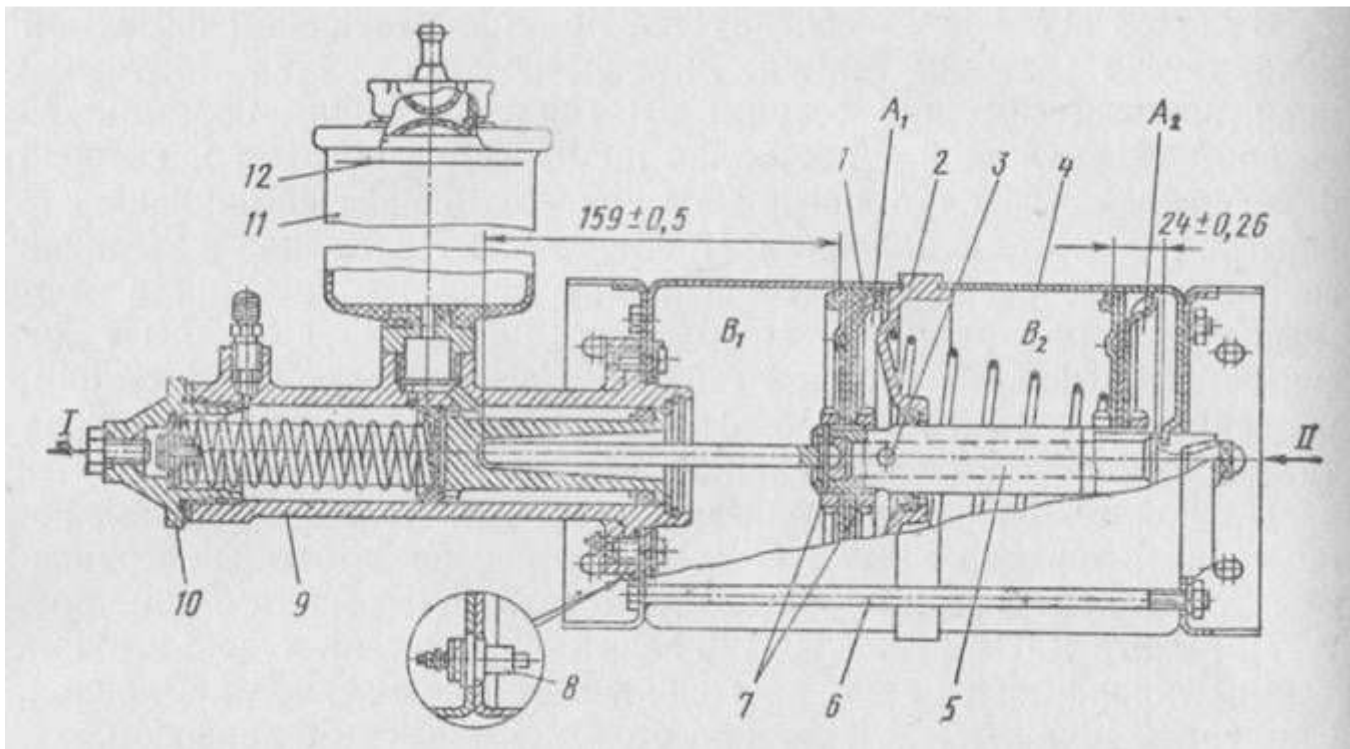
Пневматический усилитель с главным гидравлическим тормозным цилиндром: 1 — передний пневматический цилиндр; 2 — проставка; 3 — радиальное отверстие; 4 — задний пневматический цилиндр; 5 — шток с поршнями; 6 — стяжной болт; 7 — гайки штока; 8 — включатель сигнализации о неисправности тормозной системы; 9 — главный гидравлический тормозной цилиндр; 10 — пробка; 11 — бачок для тормозной жидкости; 12 — уровень жидкости
